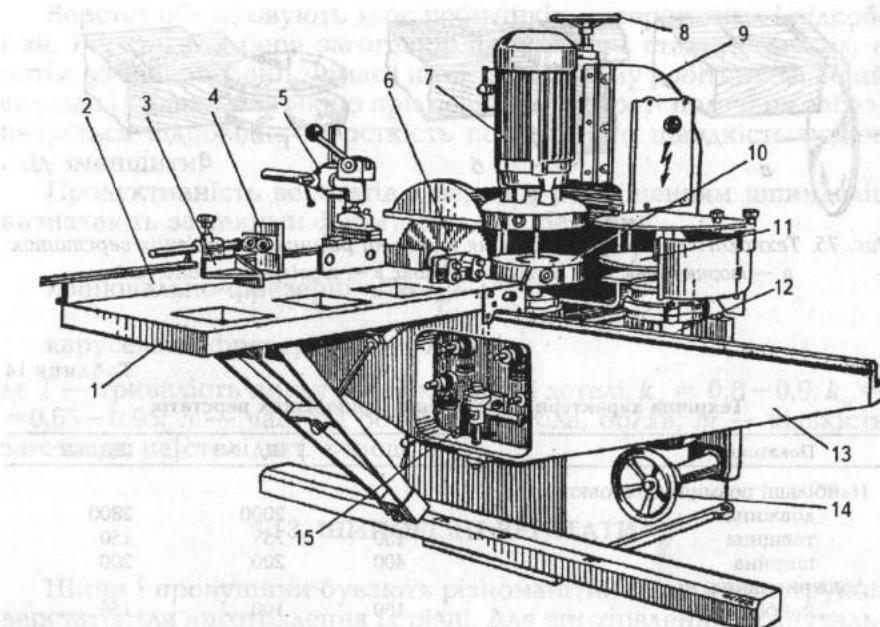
Однобічний шипорізний верстат ШО15Г-5:
